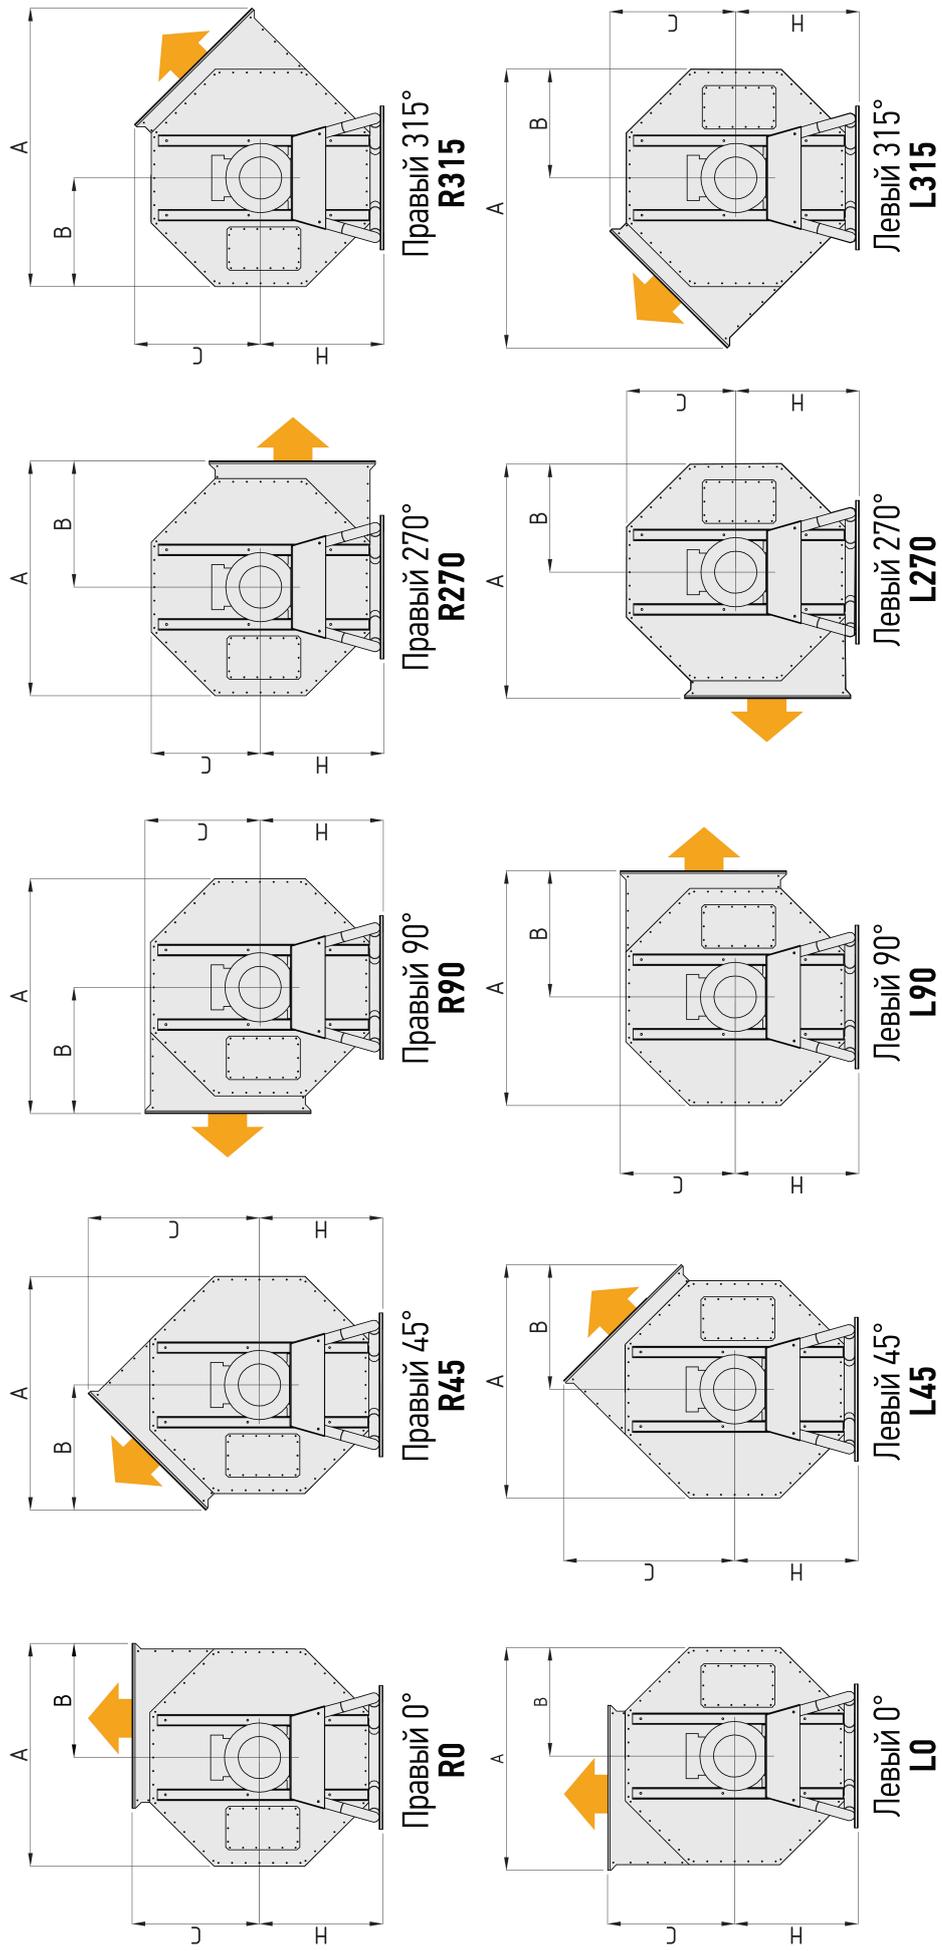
Углы установки корпуса и направление вращения рабочего колеса вентиляторов
